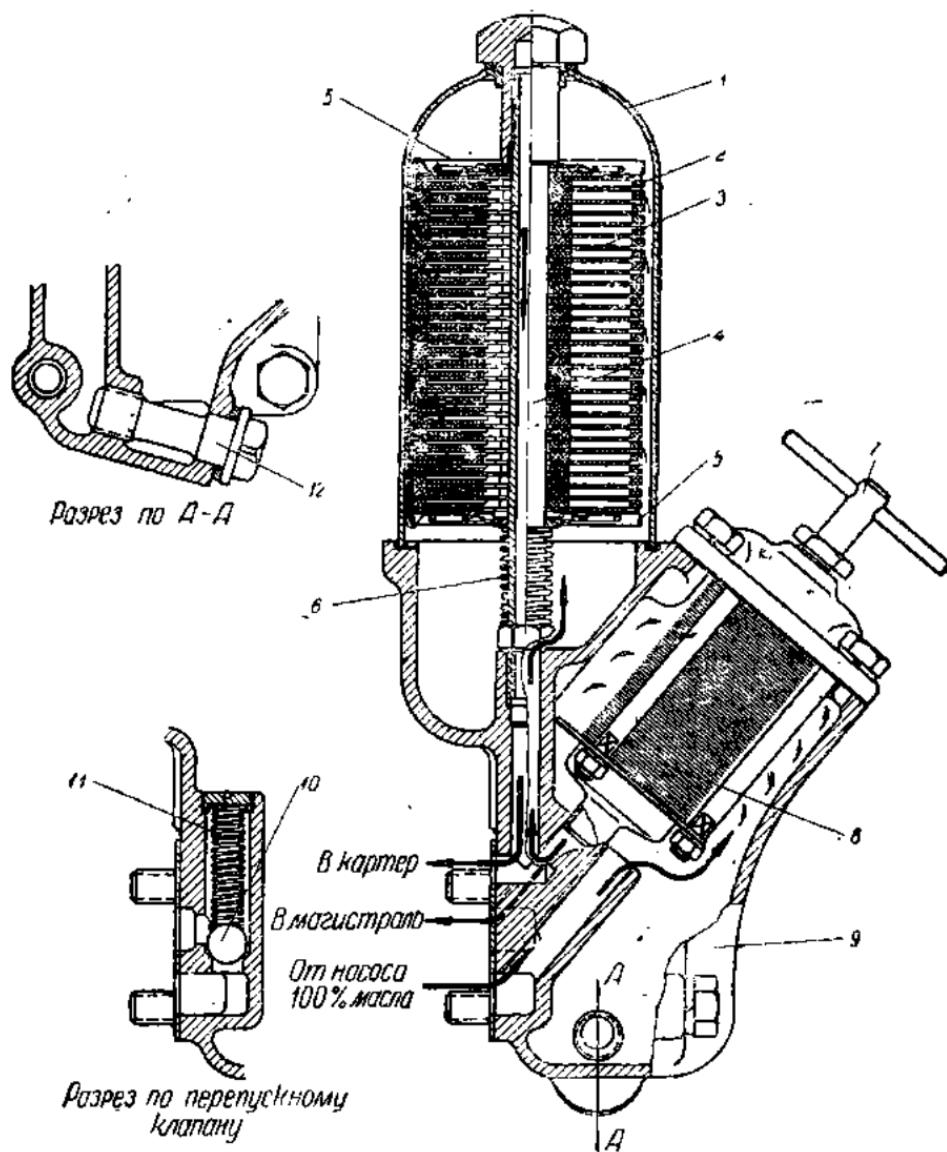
Фильтры грубой и тонкой очистки масла (1 — корпус фильтра тонкой очистки; 2 — картонные фильтрующие прокладки (звездочки); 4 — центральная трубка; 5 — верхняя и нижняя крышки патрона; 6 — пружина; 7 — рукоятка; 8 — фильтрующий пластинчатый патрон грубой очистки; 9 — корпус фильтра; 10 — перепускной клапан; 11 — пружина клапана; 12 — спускная пробка).
